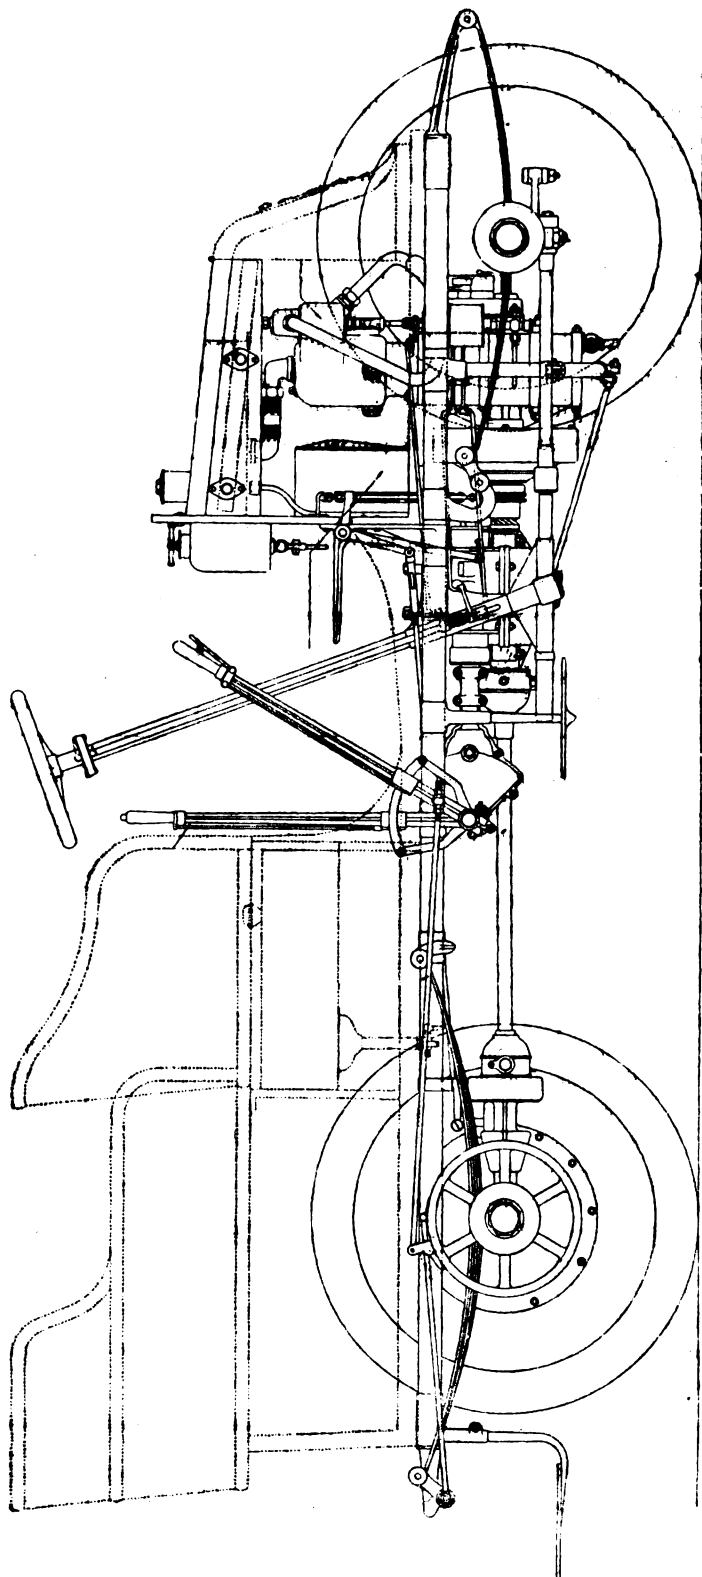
Vue en élévation de la voiture Benoit frères.
